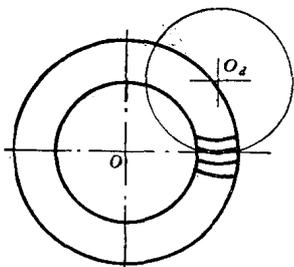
零度螺旋锥齿轮 (圆弧齿)
